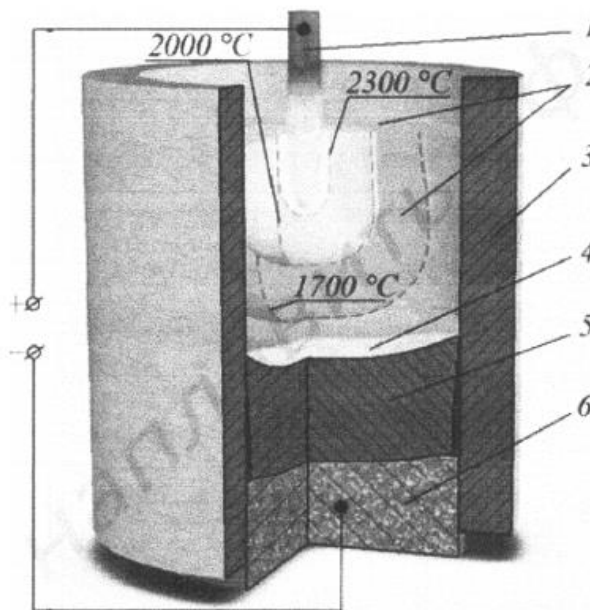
Топологія температурного поля в шлаковій ванні: 1-плавкий електродний дріт; 2-шлакова ванна; 3-кристалізатор; 4-ванна розплаву; 5-наплавлений метал; 6-виріб.
